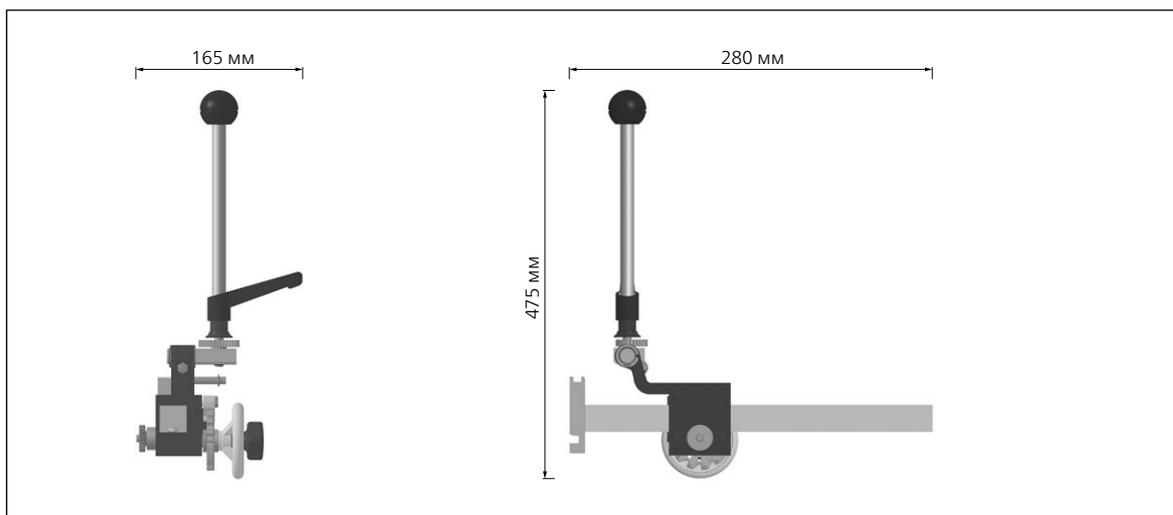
Устройство HV 161, вид сверху, размеры в мм
